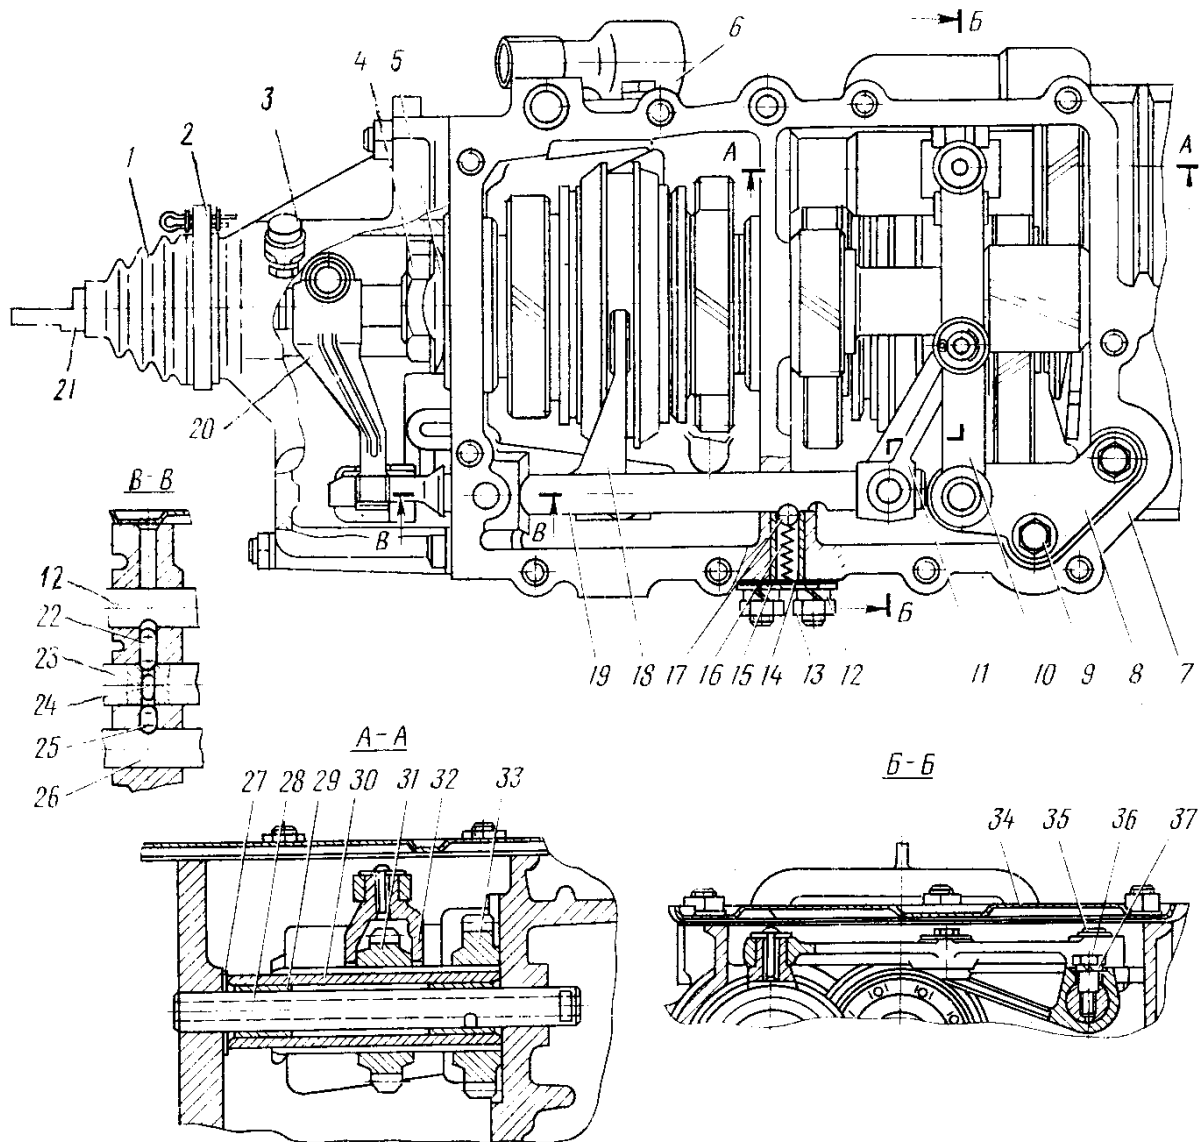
Коробка передач (вид сверху, верхняя крышка снята): 1 — чехол ползуна; 2 — хомут; 3 — сапун; 4 — гайка крепления промежуточного вала; 5 — отгибная шайба; 6 — редуктор привода спидометра; 7 — картер коробки передач; 8 — кронштейн механизма включения заднего хода; 9, 36 — болты; 10 — рычаг переключения заднего хода; 11 — поводок рычага переключения заднего хода; 12, 37 — пружинные шайбы; 13 — гайка; 14 — крышка фиксатора; 15 — прокладка крышки; 16 — пружина фиксатора; 17 — шарик фиксатора; 18 — вилка переключения III и IV передач; 19 — шток переключения заднего хода; 20 — ползун переключения передач; 21 — шток ползуна; 22 — замок верхних штоков; 23 — шток вилки переключения III и IV передач; 24 — толкатель замков; 25 — замок нижних штоков; 26 — шток вилки переключения I и II передач; 27 — упорная шайба; 28 — ось шлицевого вала; 29 — втулка оси шлицевого вала; 30 — шлицевой вал ведущей шестерни заднего хода; 31 — промежуточная ведущая шестерня заднего хода; 32 — вилка включения заднего хода; 33 — промежуточная ведомая шестерня заднего хода; 34 — верхняя крышка коробки передач; 35 — стопорное кольцо оси рычага заднего хода.
